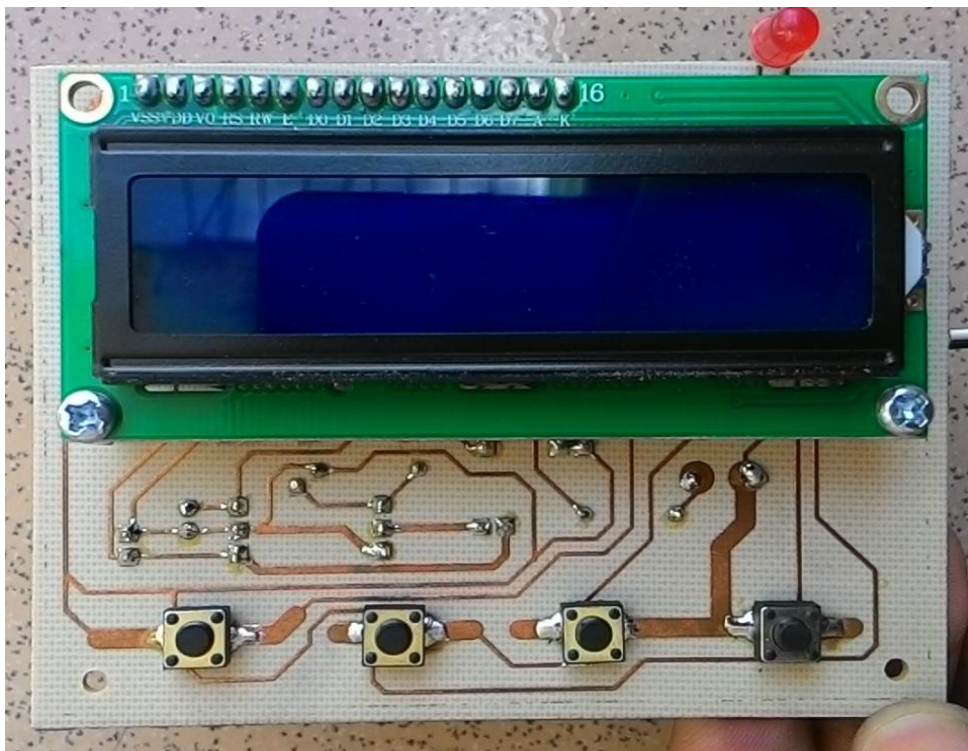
Layout PCB ATmega 8535 Keseluruhan
